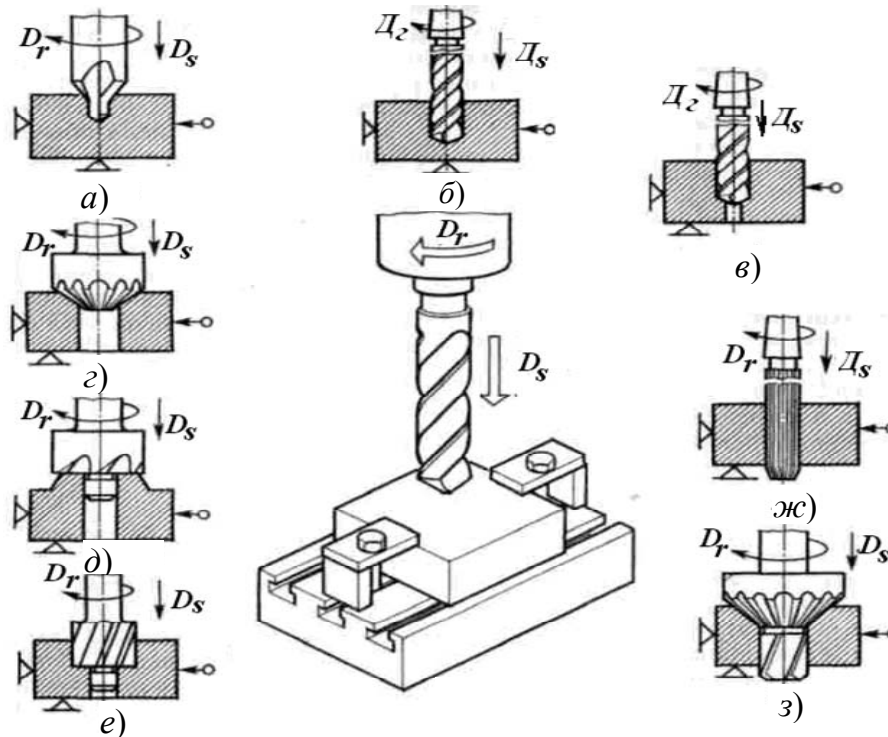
Эскизы схем обработки: комбинированным центровочным сверлом (а); винтовым сверлом (б); зенкером (в); зенковкой (г); цековкой (д), (е); разверткой (ж); комбинированным инструментом (з)
